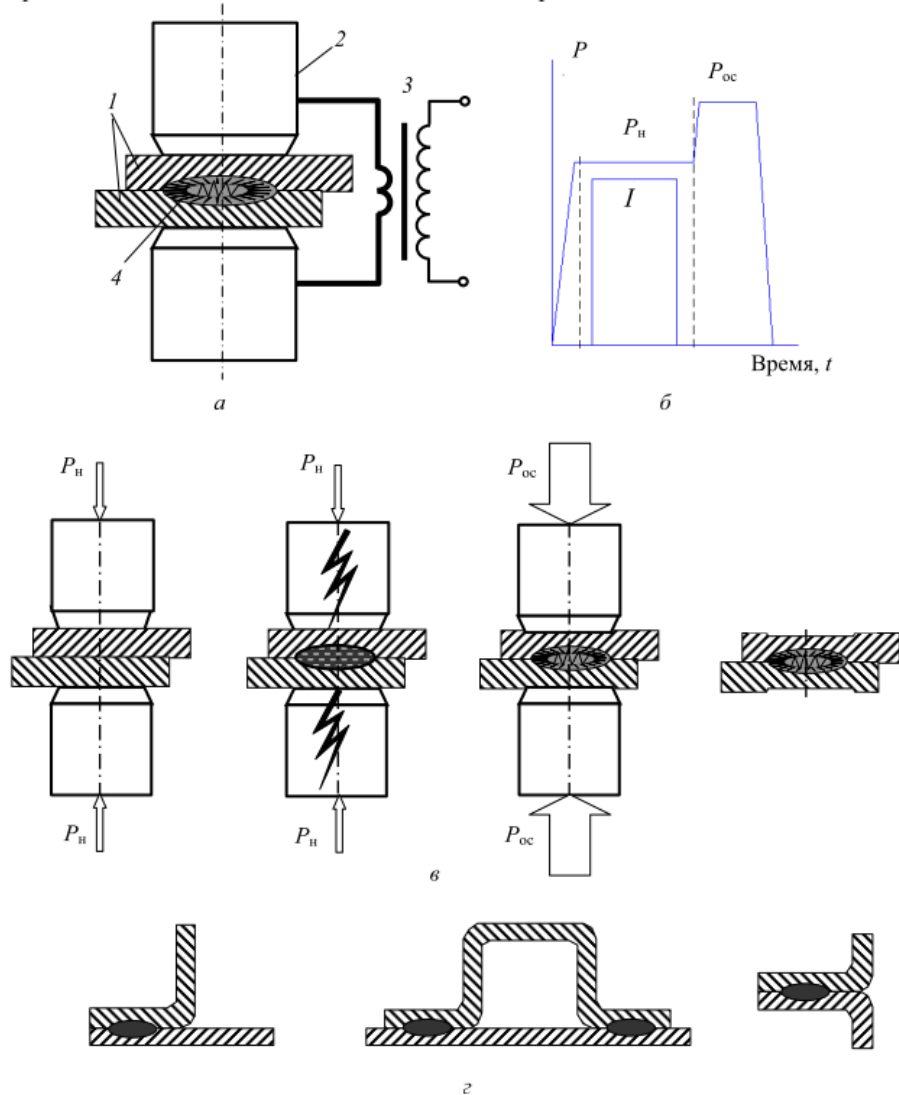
Точечная контактная сварка: а – схема сварки; б – циклограмма; в – стадии сварки; г – типы сварных соединений
